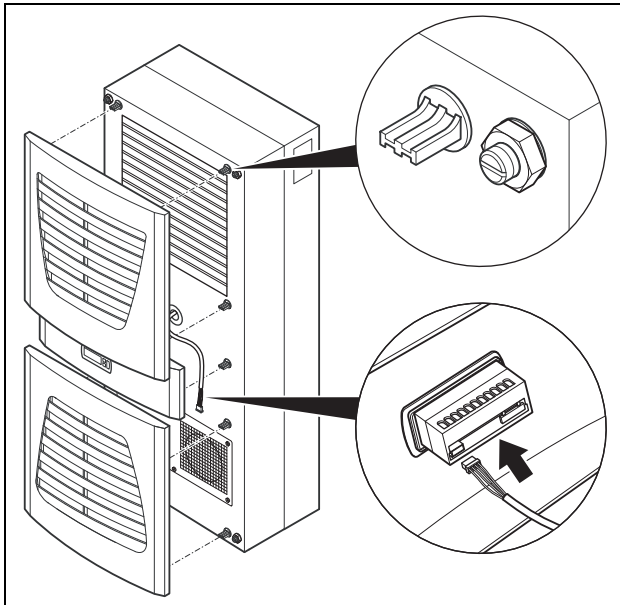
Brancher l'afficheur et mettre la grille à lamelles en place
